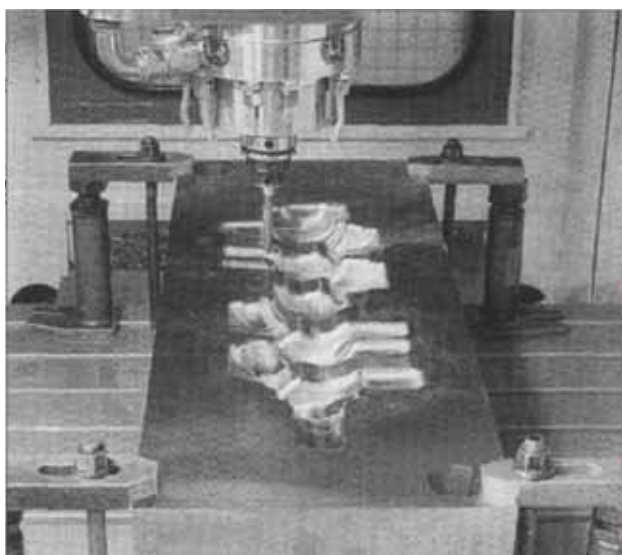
Usinagem em HSC do molde para virabrequim.
